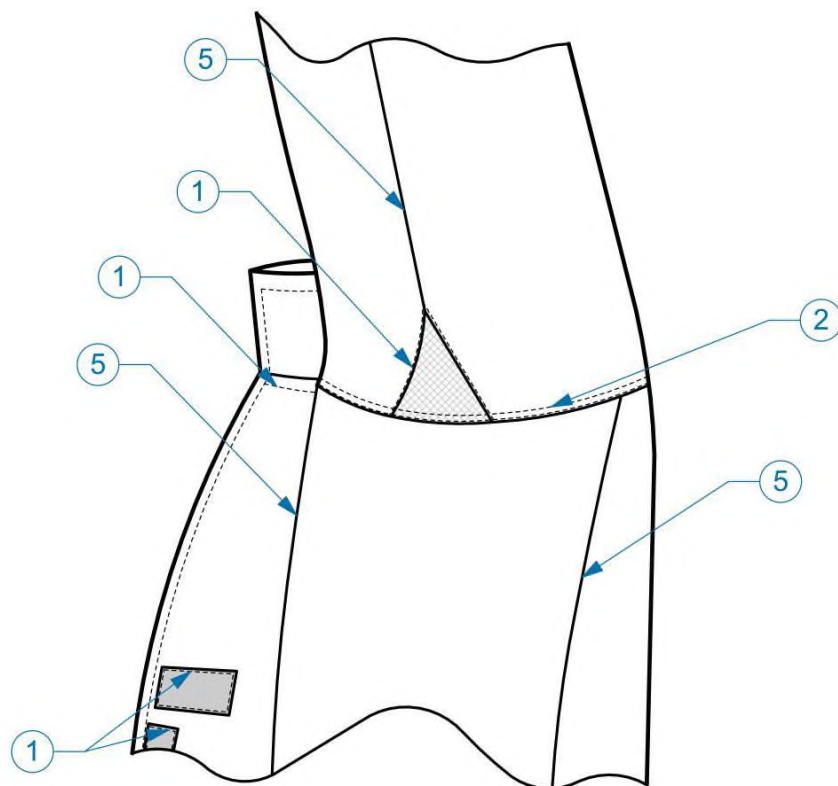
Строчки предмета (вид збоку)/
